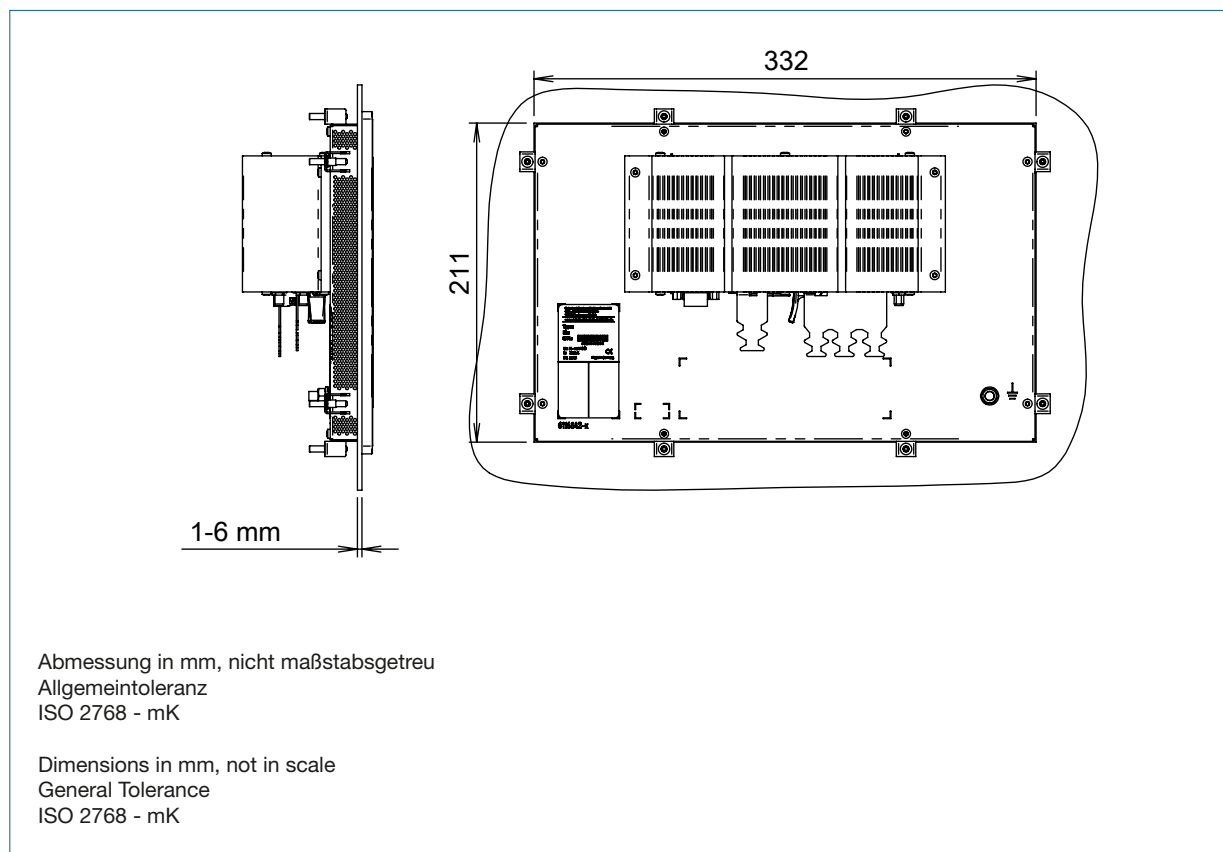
13,3" Prime Panel Pico Einbau - Einbauausschnitt
